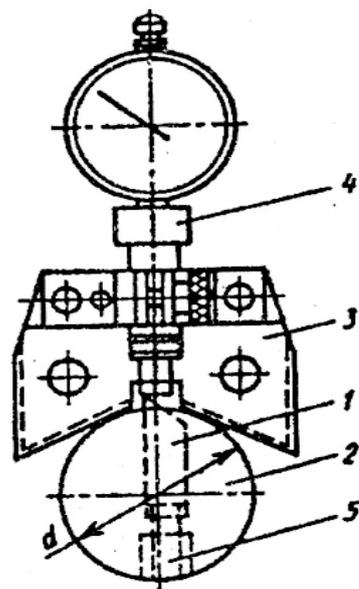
Магнитный прибор с призмой с выключением магнитов для установки и настройки резцов на размер: 1 – резец; 2 – борштанга; 3 – магнитный прибор с выключением магнита; 4 – индикатор прибора; 5 – упорно-регулирующий винт
